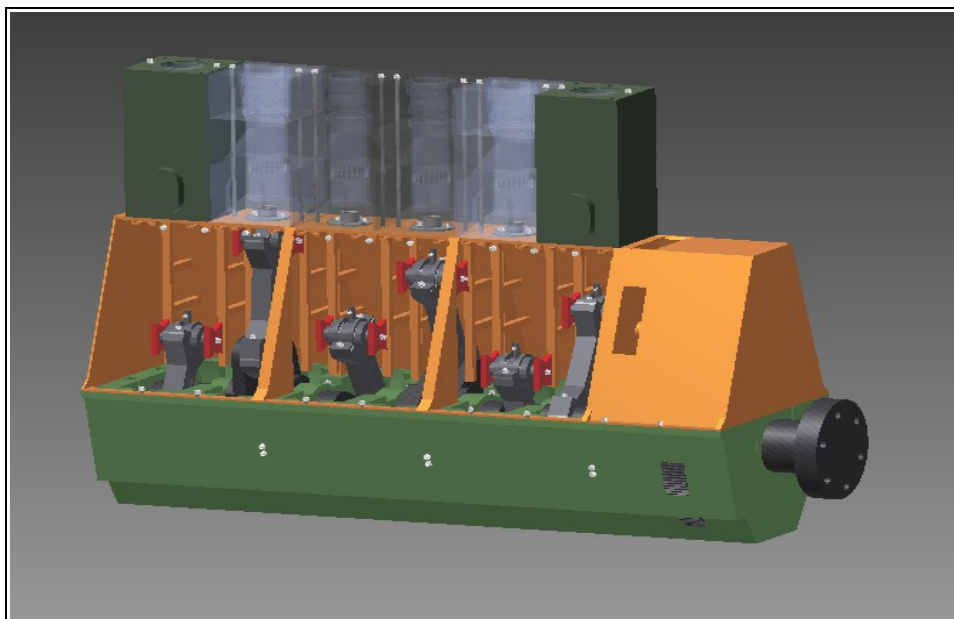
Bloque de cilindros con motor, ensamble
